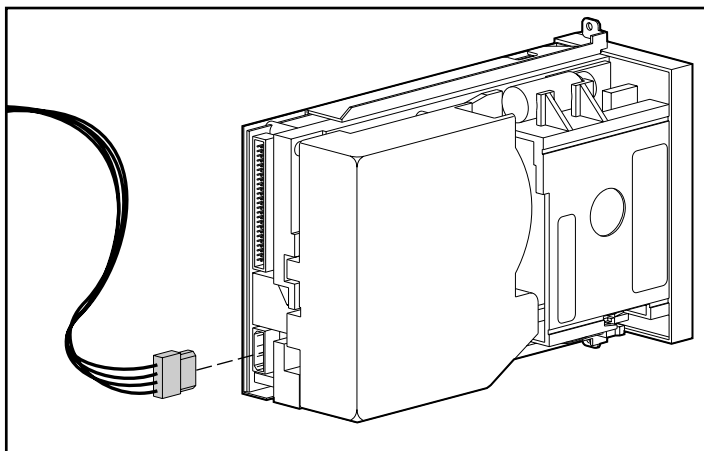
Collegamento del cavo di alimentazione all'unità DLT
